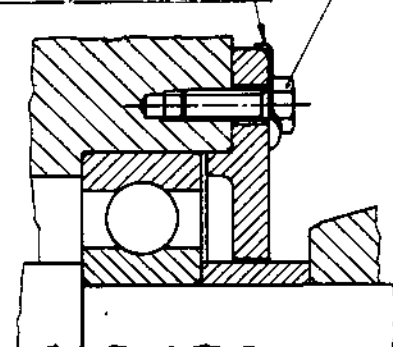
Bloccaggio di cuscinetto volante per mezzo di coperchietto con battuta di centraggio, fissato con vite a testa esagonale (gambo interamente filettato) e rosetta di sicurezza.
